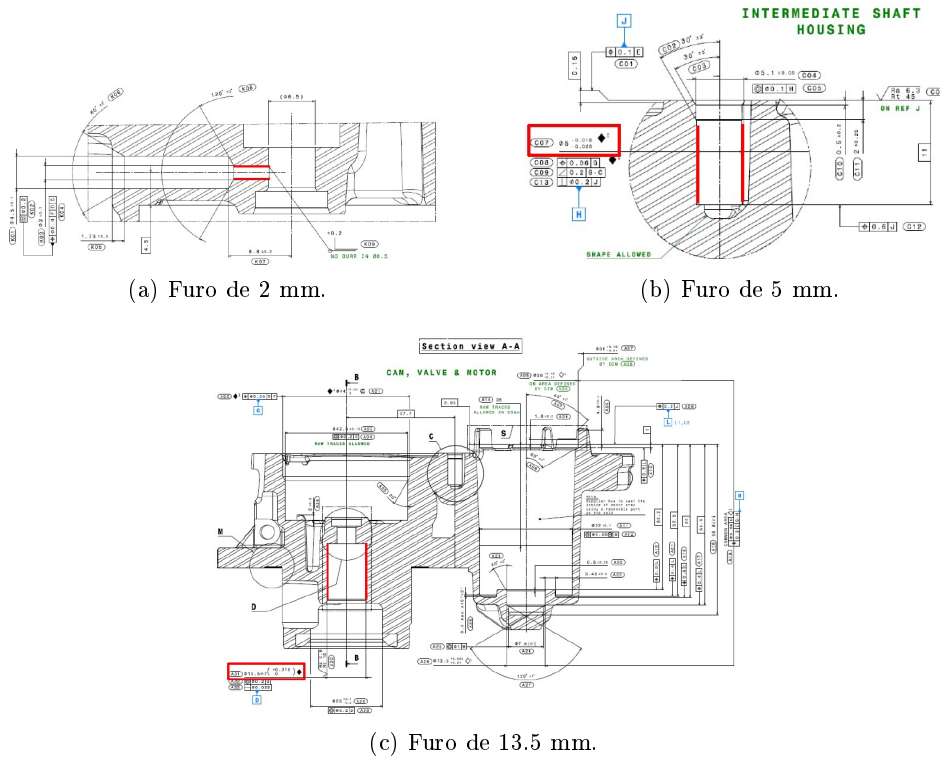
Furos a realizar o controlo dimensional ou de obstrução.
